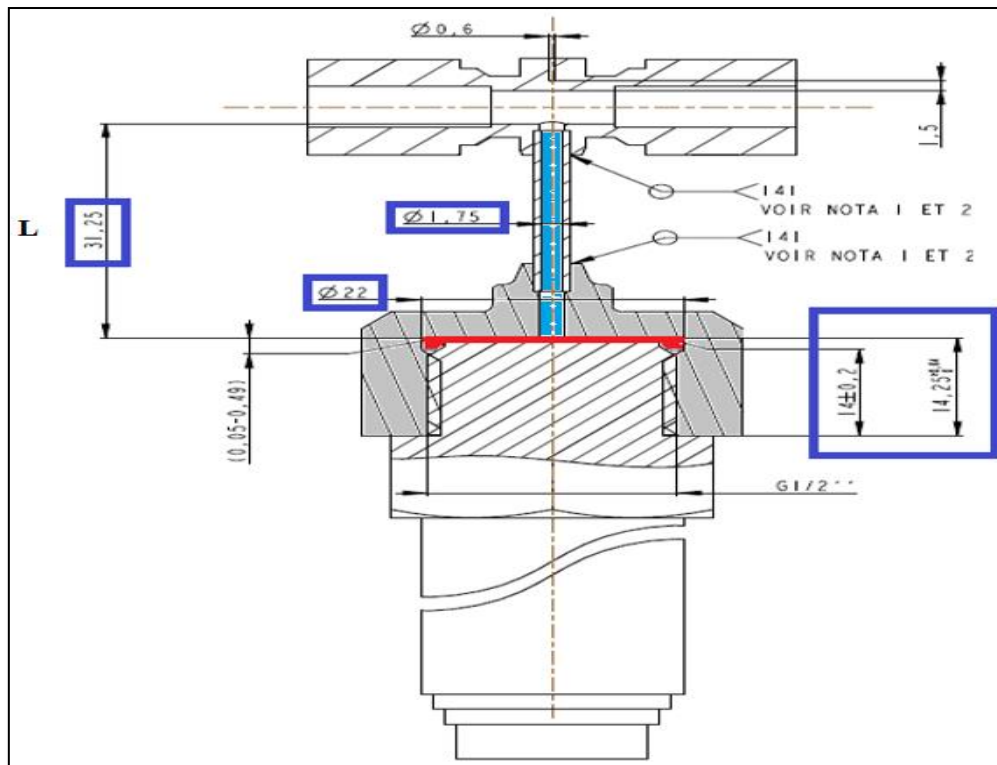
Plan d'intégration d'un capteur de pression : montage en cavité.
